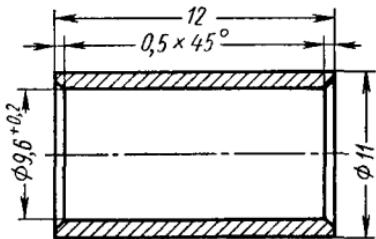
Обжимное кольцо для трубки слива топлива из головок цилиндров
